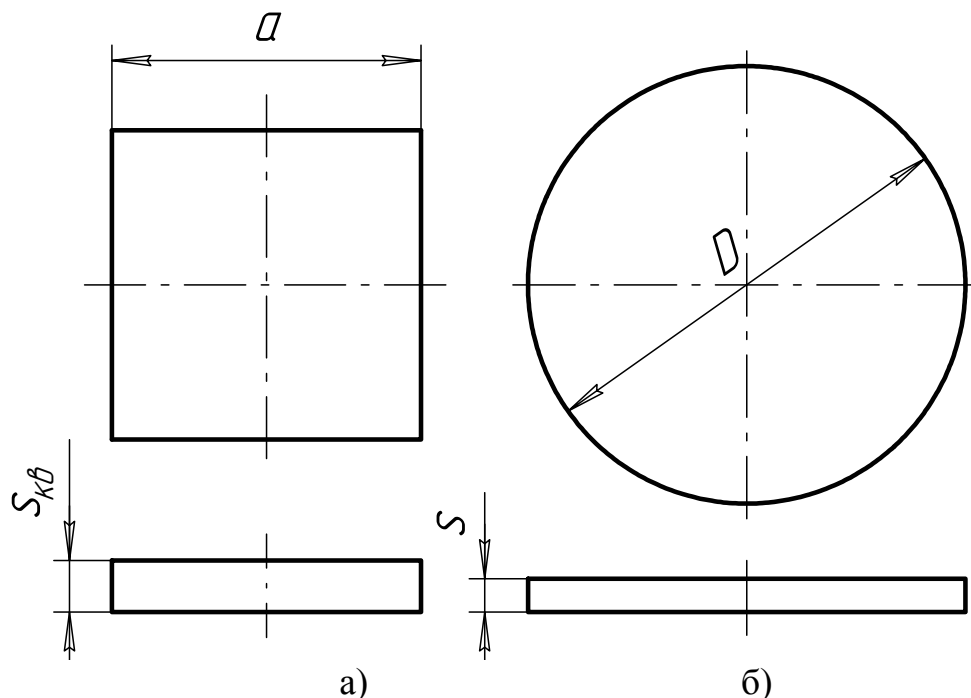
Заготовка (а) та деталь (б), що отримується процесом переформування квадратних заготовок у круглі
